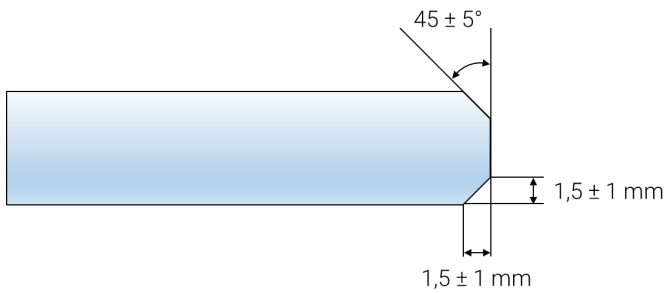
Saumtoleranz für Kantenbearbeitung (Eckelt Standard)
